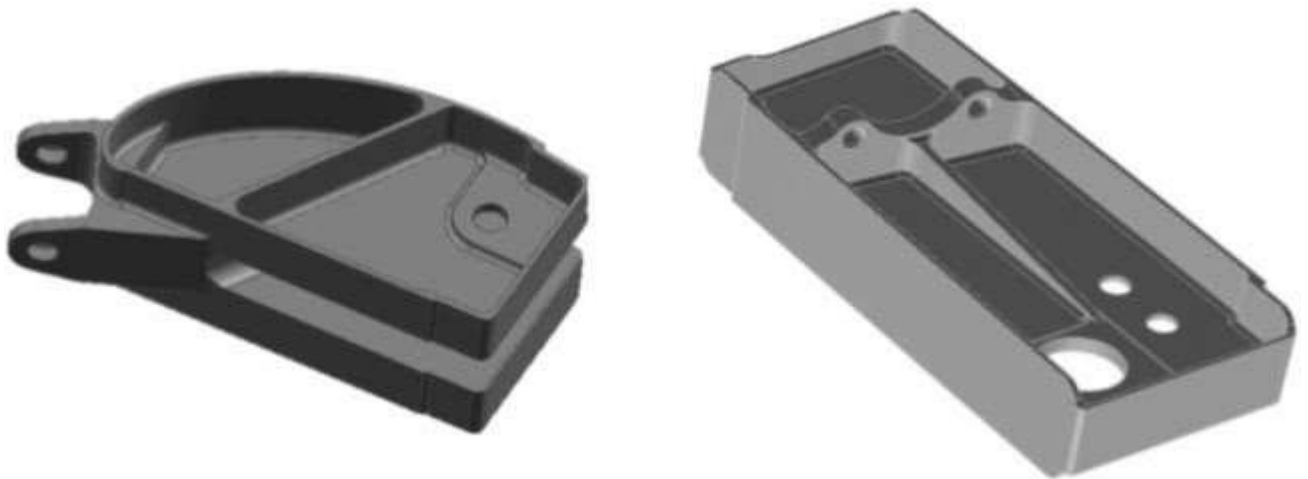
Типовые детали из алюминиевых сплавов
